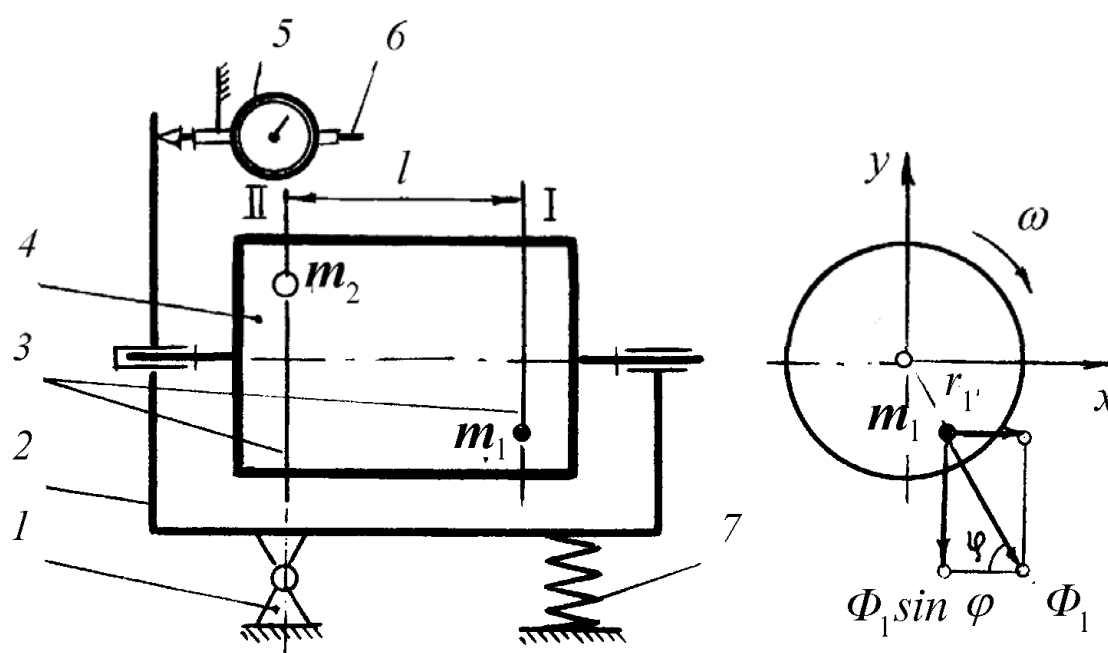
Балансировка ротора на примере станка В.В. Шитикова
